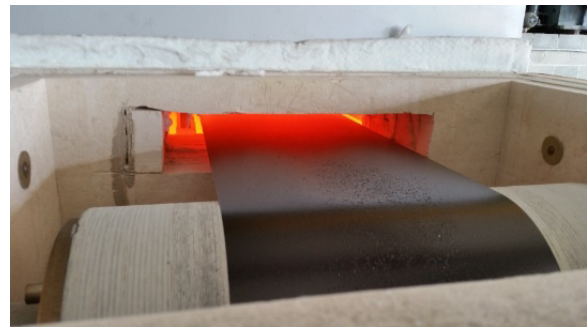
Vue d'ensemble de l'installation SprayCooling.
